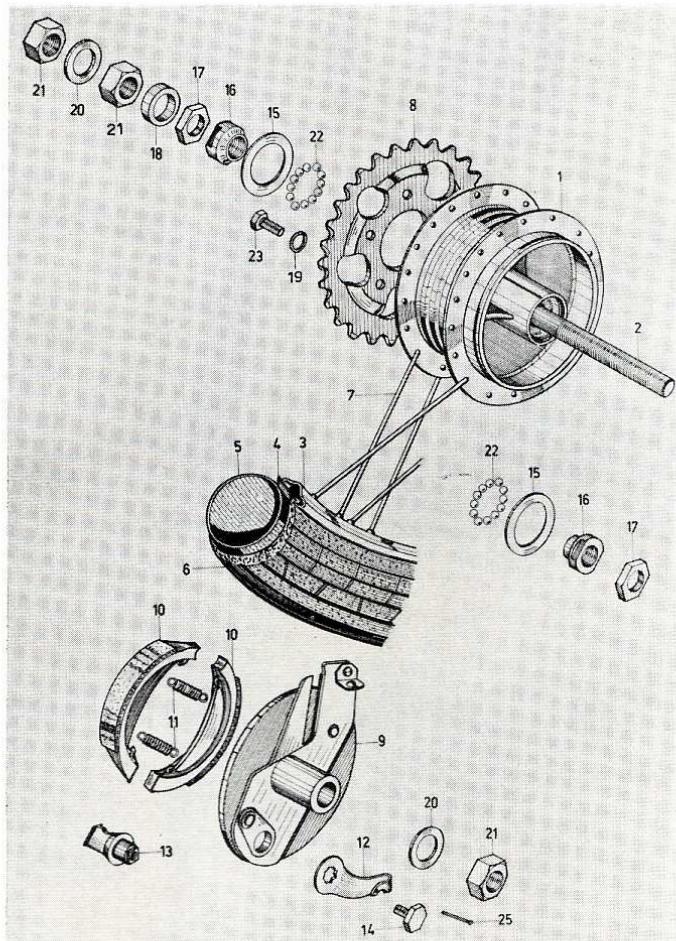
VUE ECLATEE DU MOYEU ARRIERE.
